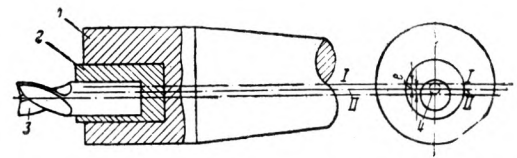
Схема регулирующего патрона для фрезерования пазов концевыми фрезерами с маятниковой подачей
